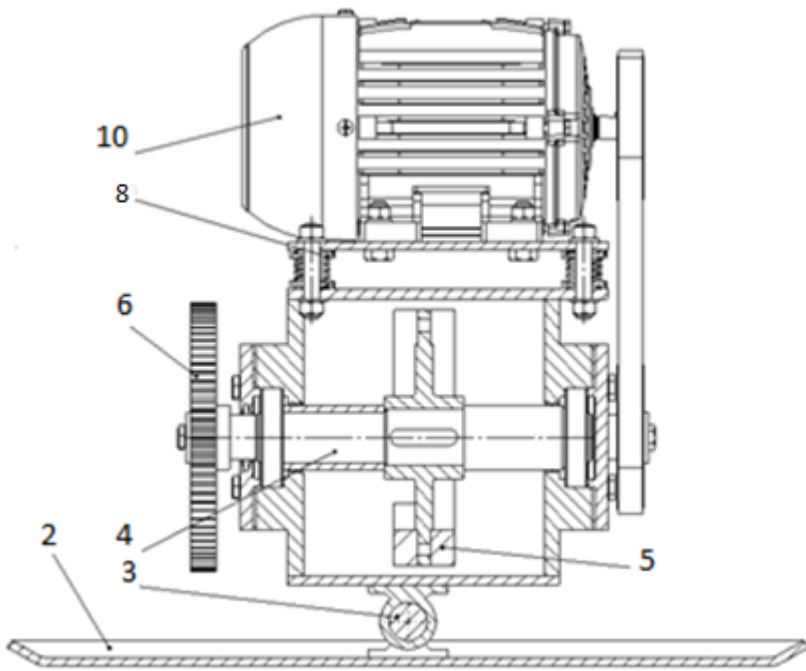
Конструктивна схема віброплити: 1 – корпус; 2 – плита; 3 – шарнірне з'єднання; 4 – вал вібратора в зборі; 5 – дебалансний вібратор; 6 – зубчаста передача; 7 – кришка корпусу; 8 – пружні опори; 9 – пасова передача; 10 – електродвигун
